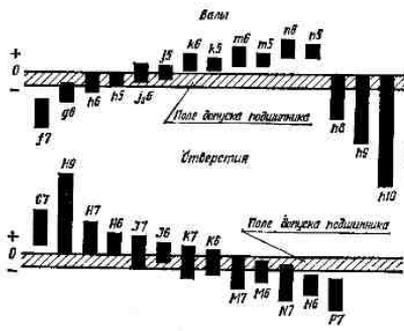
Схема расположения полей допусков валов и отверстий для различных посадок
